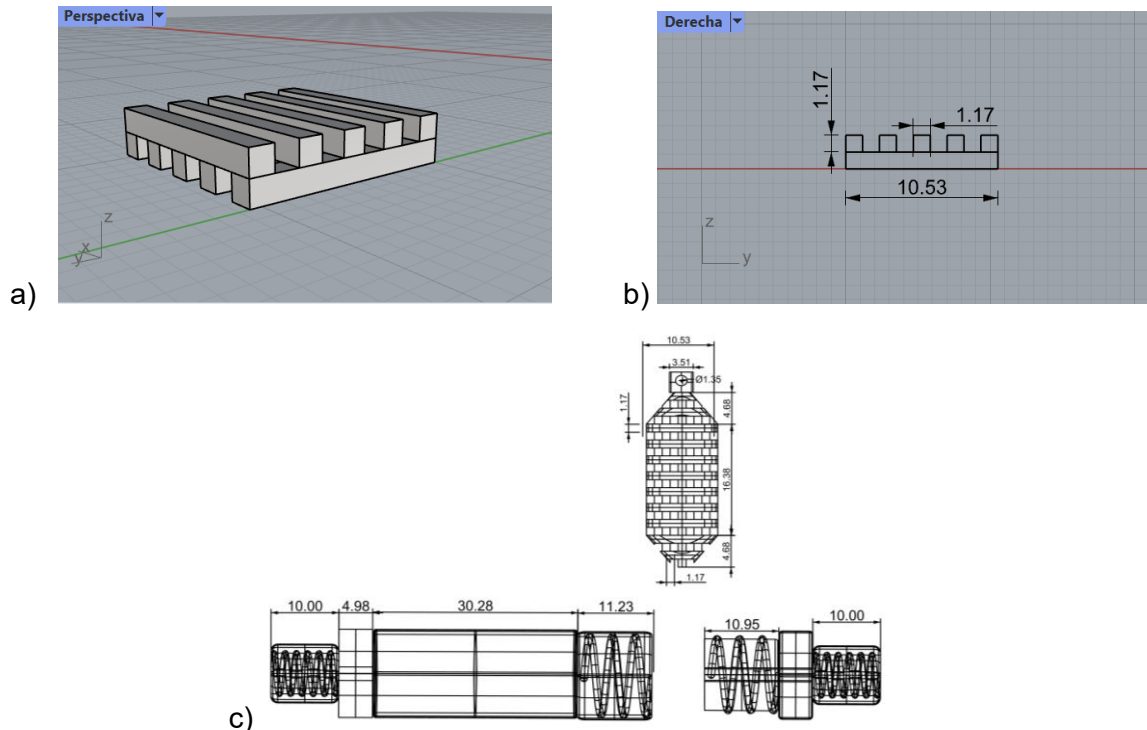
a) Diseño de los cuboides; b) Dimensiones de los cuboides y de los canales interiores; c) Diseño y dimensiones del dispositivo completo y del soporte del dispositivo.
